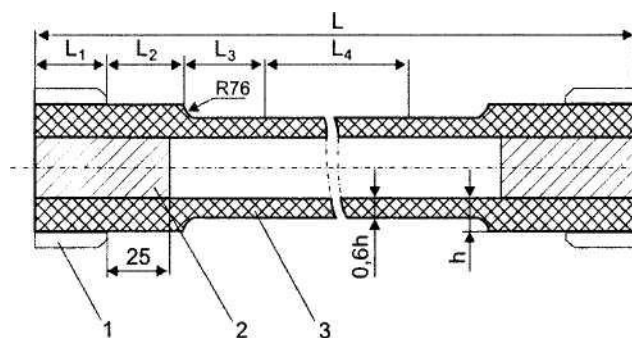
Трубчастий зразок з зовнішнім діаметром до 50 мм: 1 - зразок; 2 - металева пробка; 3 - захвати;
